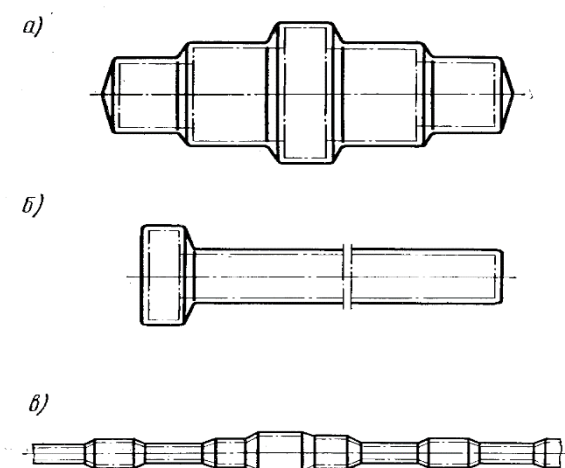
Исходные заготовки валов различного конструктивного исполнения, полученные путем штамповки в подкладных штампах (а), штамповкой на горизонтально ковочной машине (б) и поперечно-винтовой прокаткой (в)
